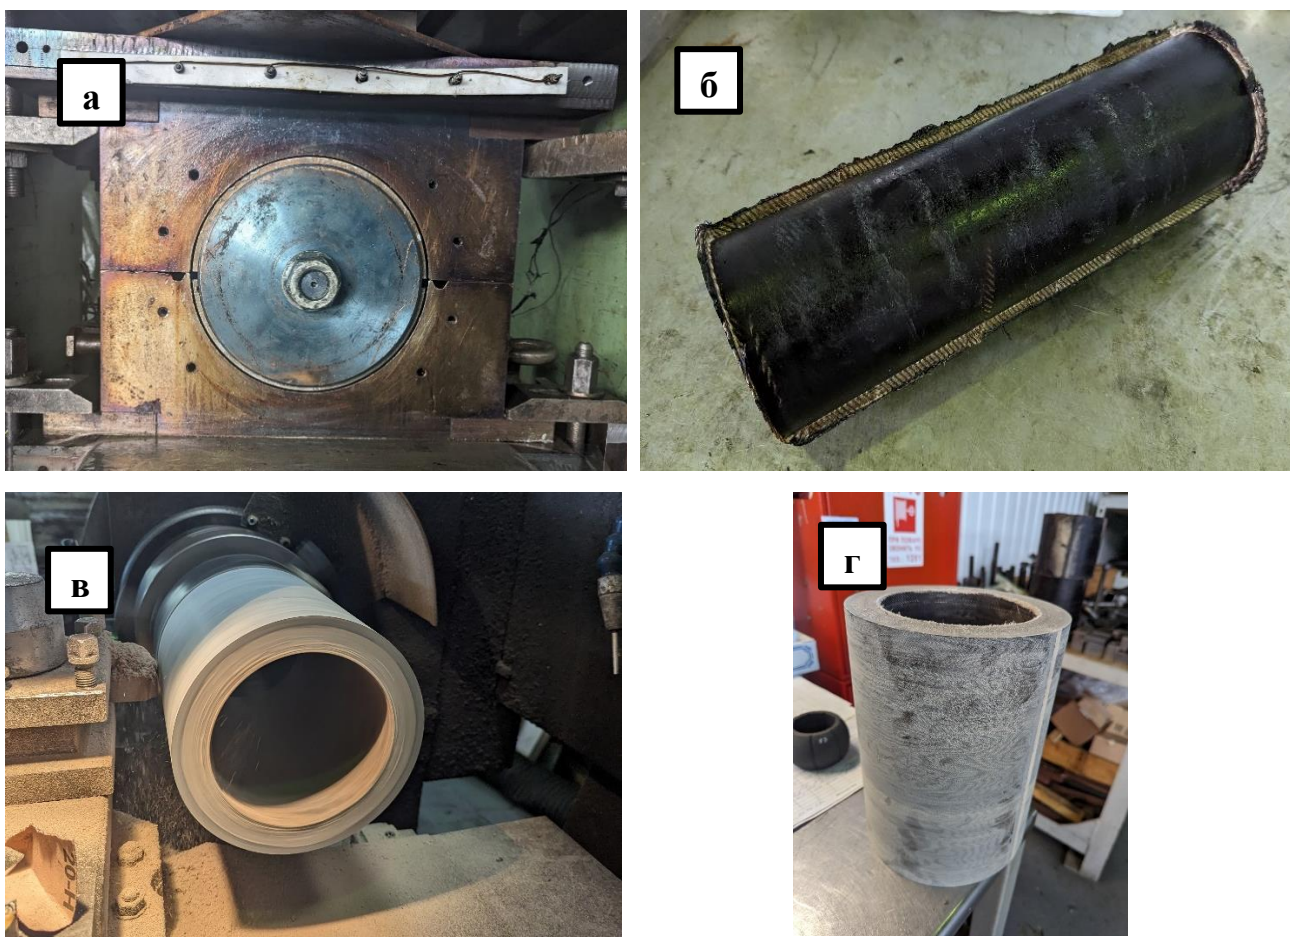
Изготовление заготовок гибридного ПКМ марки ПЭСТ-4 методом горячего прессования: а) прессование втулки $D_{\text{внутр.}} 150/155$; б) распрессованная заготовка с облоем; в) механическая обработка втулки на токарном станке; г) заготовка для изготовления рулевых накладок после механической обработки
